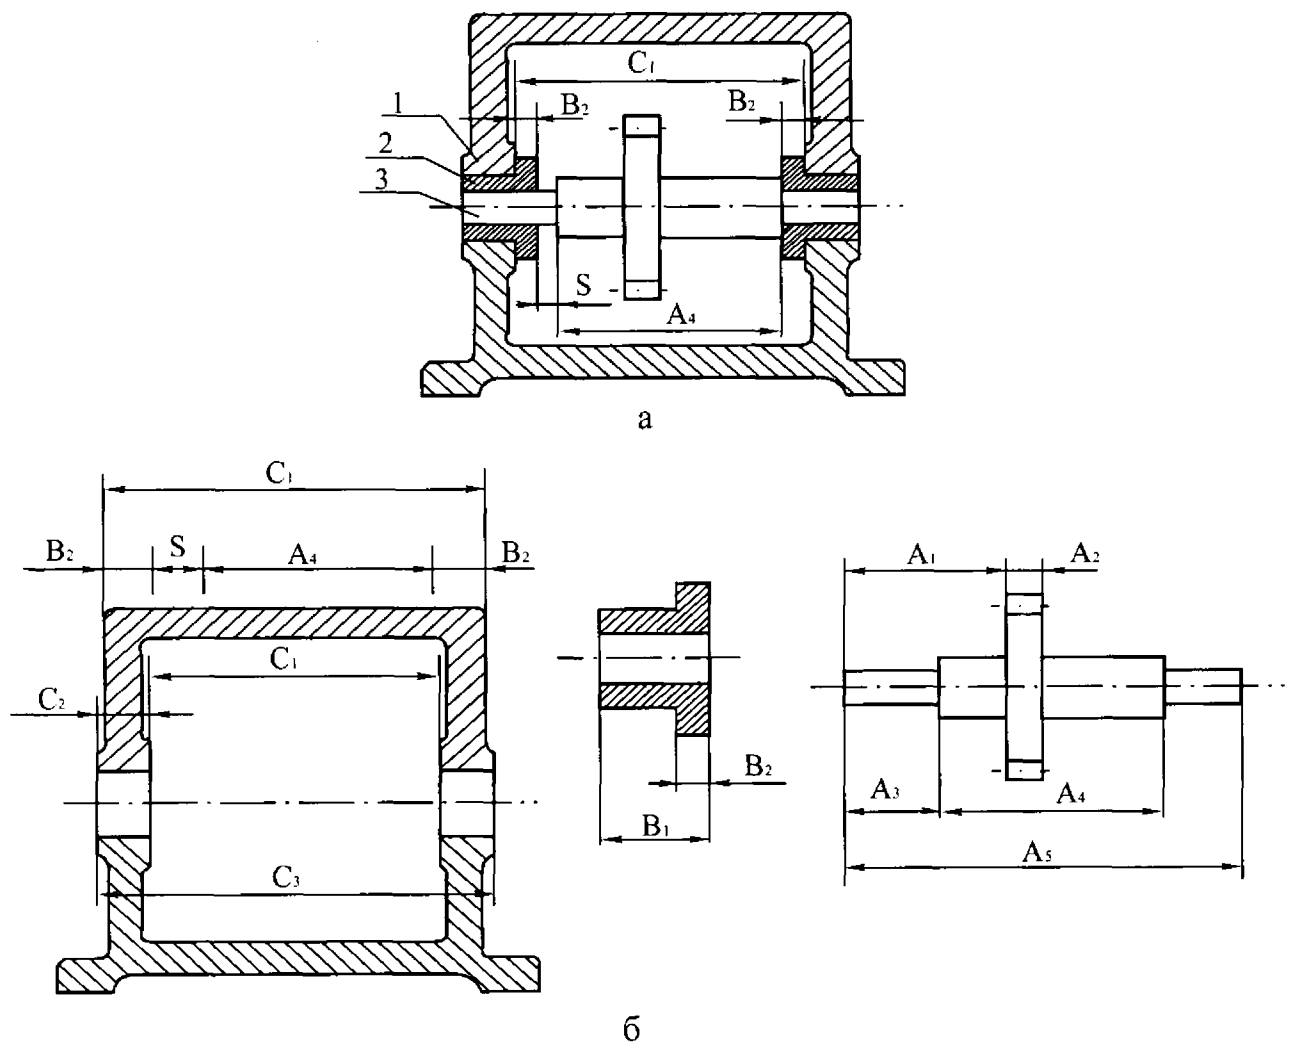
Розріз редуктора та креслення деталей, які входять у вузол.
